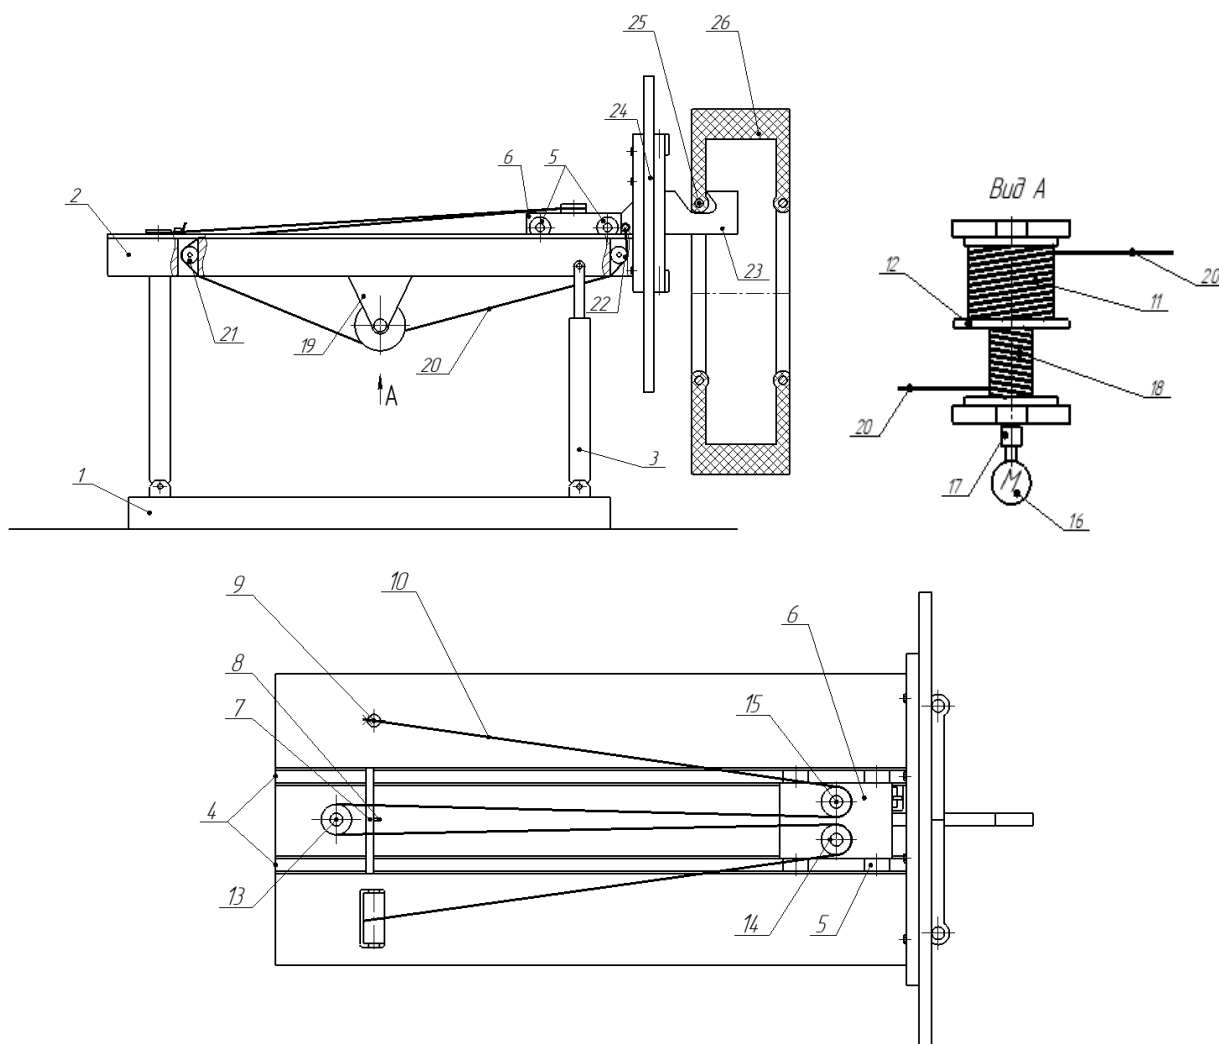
Общий вид установки для извлечения бортовых колец [99]
